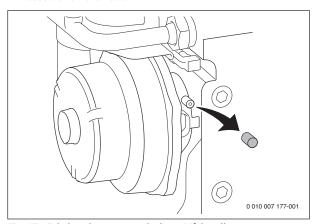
Tubulure de mesure sur le dispositif de mélange
